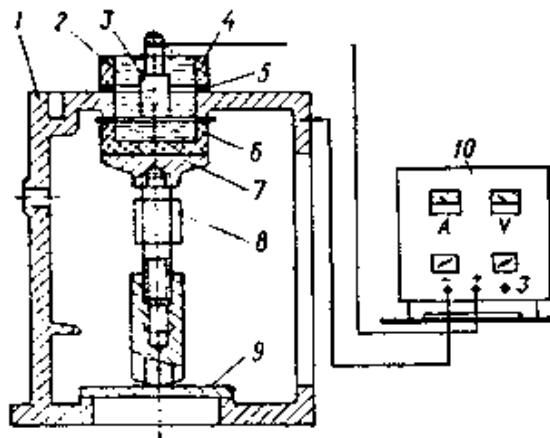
Схема місцевого електролітичного нарощування поверхні отвору в корпусній деталі:
